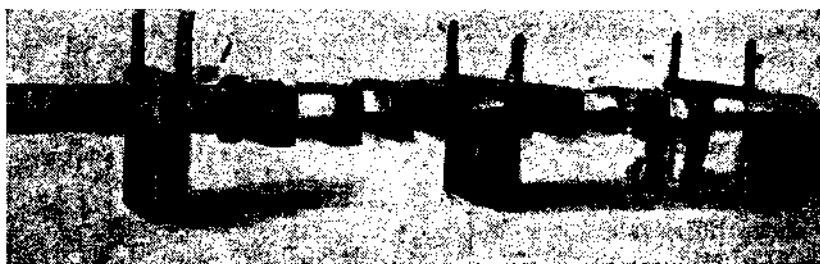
Излом коленчатого вала в плече колена, разделанный и подготовленный к сварке.
